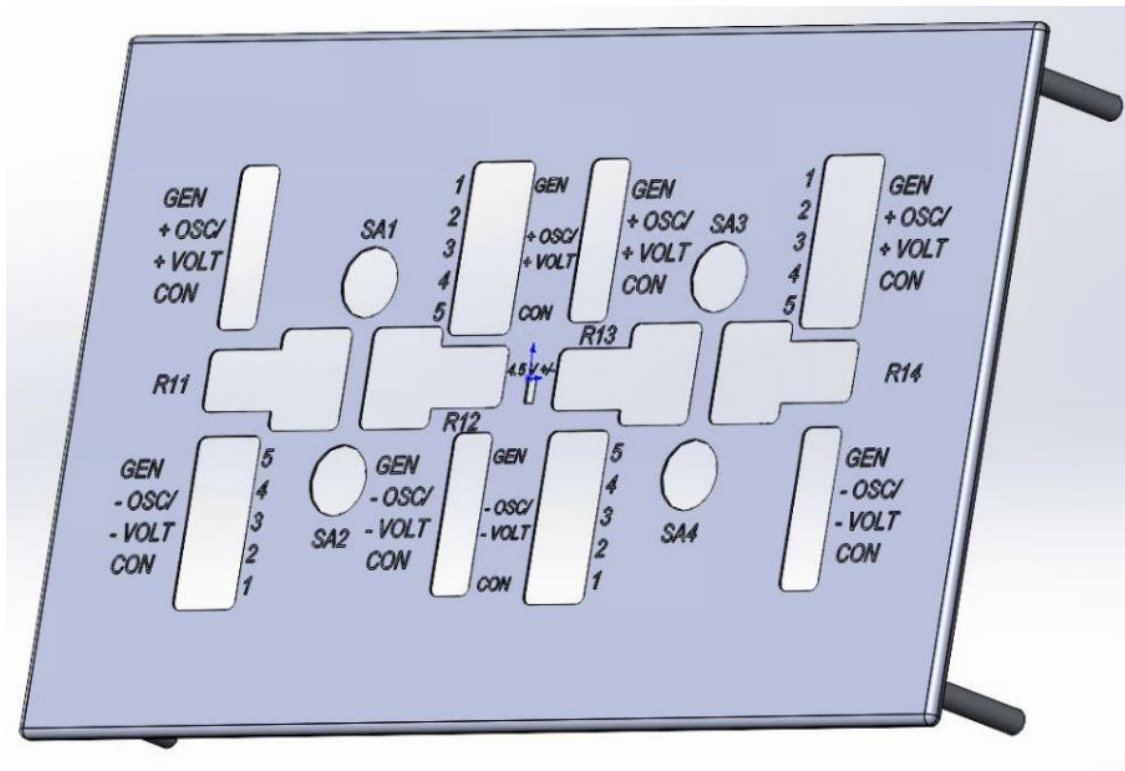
Кришка для корпусу лабораторного макету
